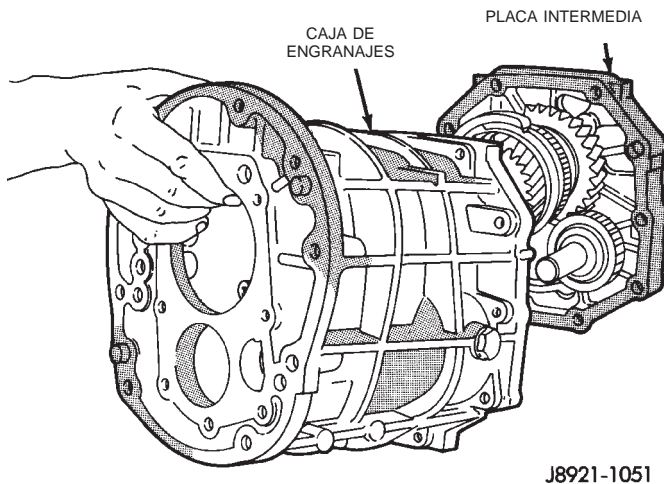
Instalación de la caja de engranajes de la transmisión en la placa intermedia
